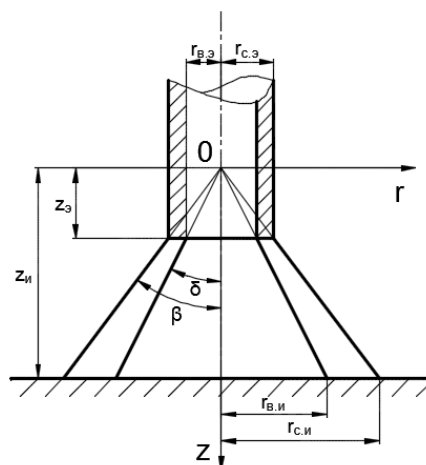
Схема горения дуги при сварке порошковой проволокой
